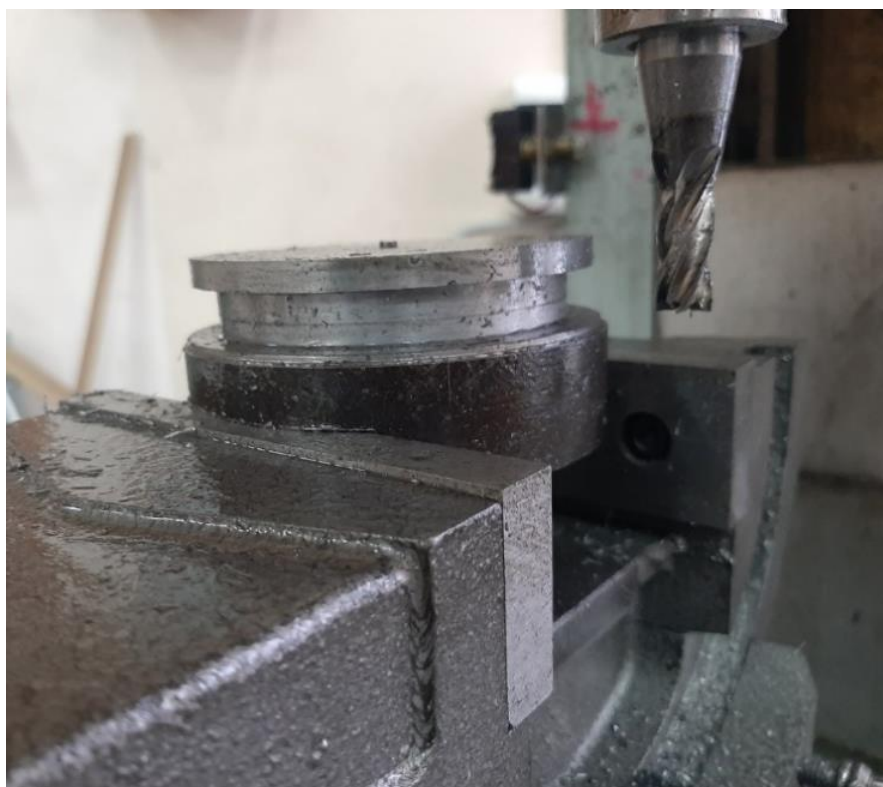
Фреза и заготовка перед началом обработки
